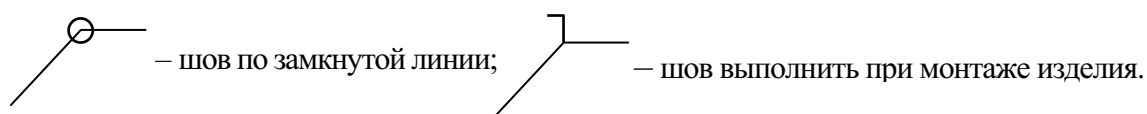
Структура условного обозначение сварного шва
